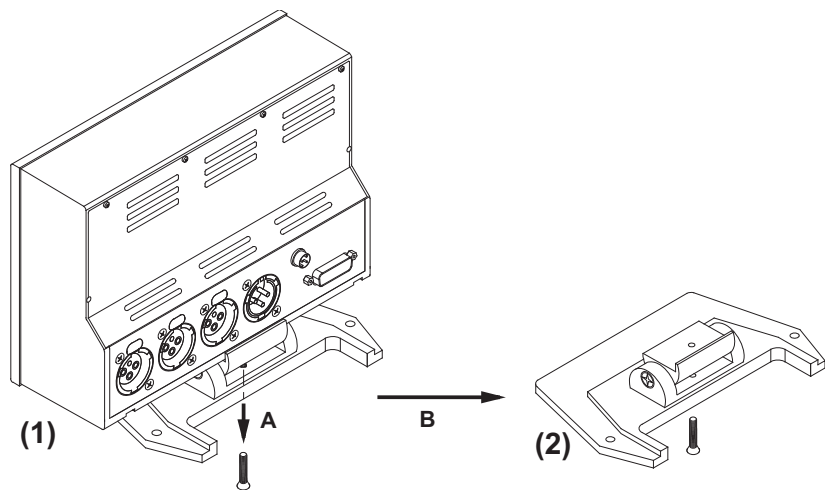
Entfernen des Tischfußes (106nX-PLUS)
